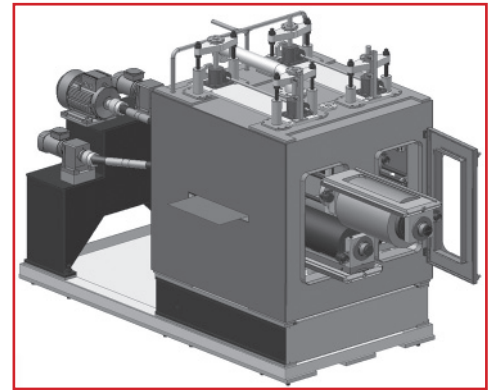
WSP-Bürstmaschine für Metallbänder und hohe Bürstkräfte
